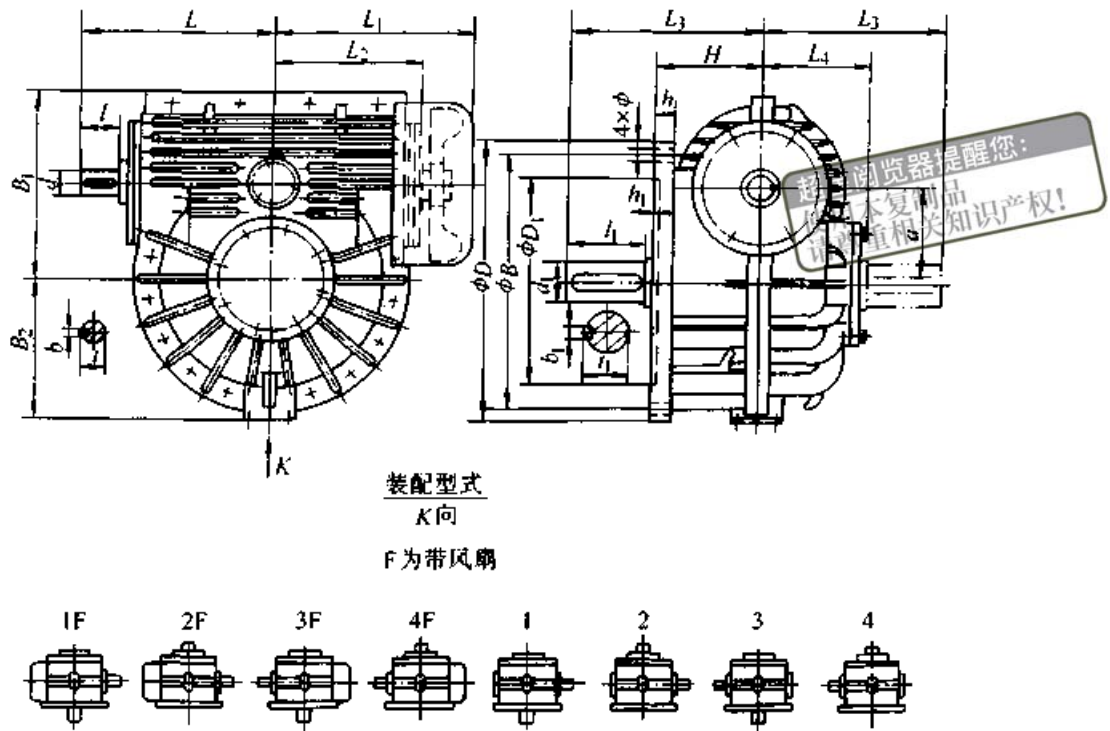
TPS 型减速器外形尺寸及装配型式
